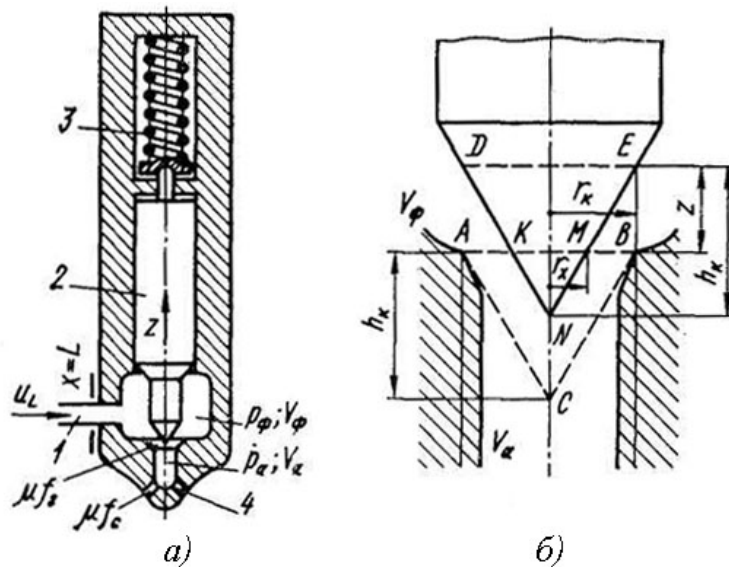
Схема форсунки закрытого типа: 1 — нагнетательный трубопровод; 2 — игла; 3 — пружина; 4 — сопловые отверстия
